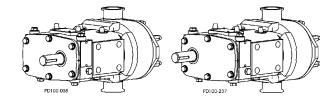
Montage latéral gauche et droit (vu depuis le couvercle de la pompe)
